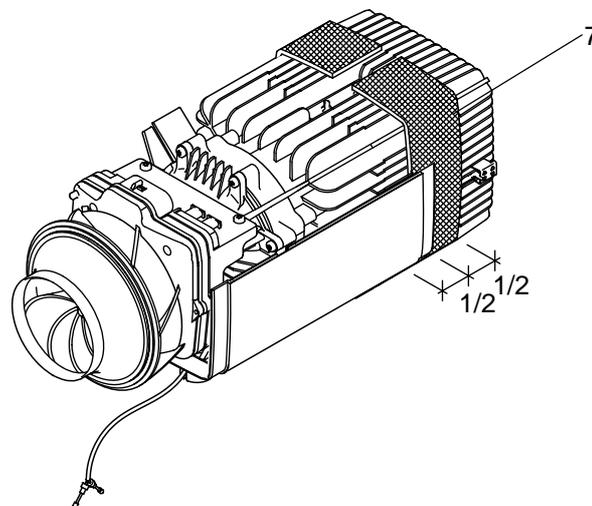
Entfernen / Aufsetzen der Gehäuseteile
